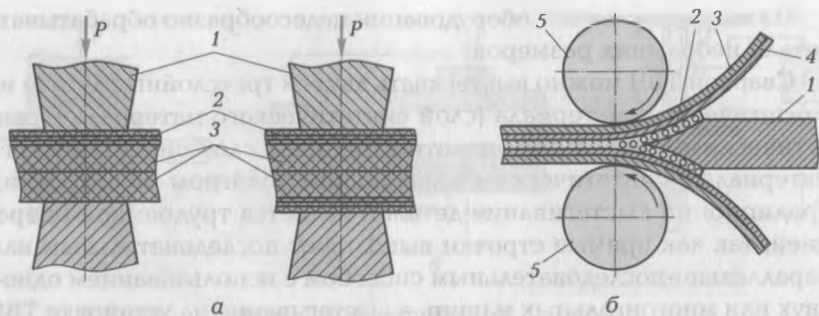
Схема сварки термоконтактным способом:
